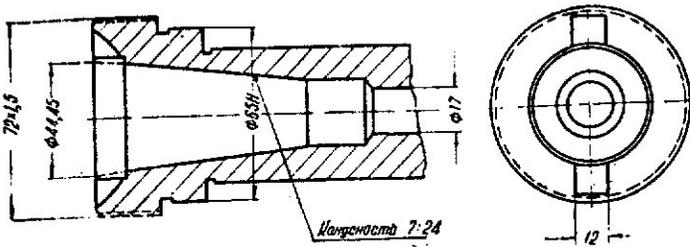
Эскиз конца шпинделя поворотной головки станка модели 6M82Ш
